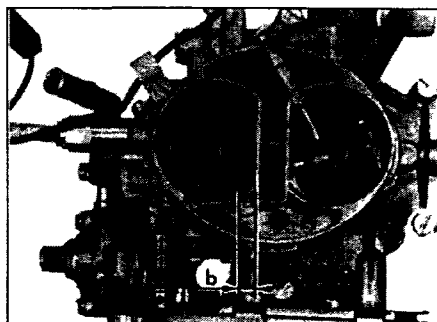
Проверка открытия воздушной заслонки (b)
